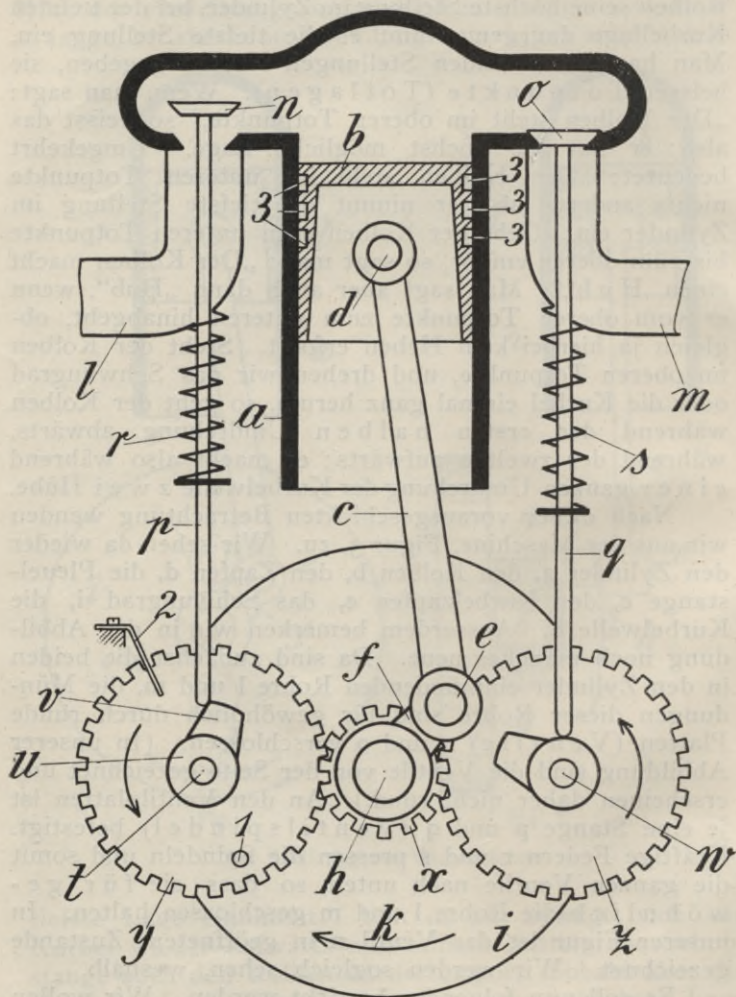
Schema des Viertaktmotors mit gesteuertem Saugventil (Schnitt).
